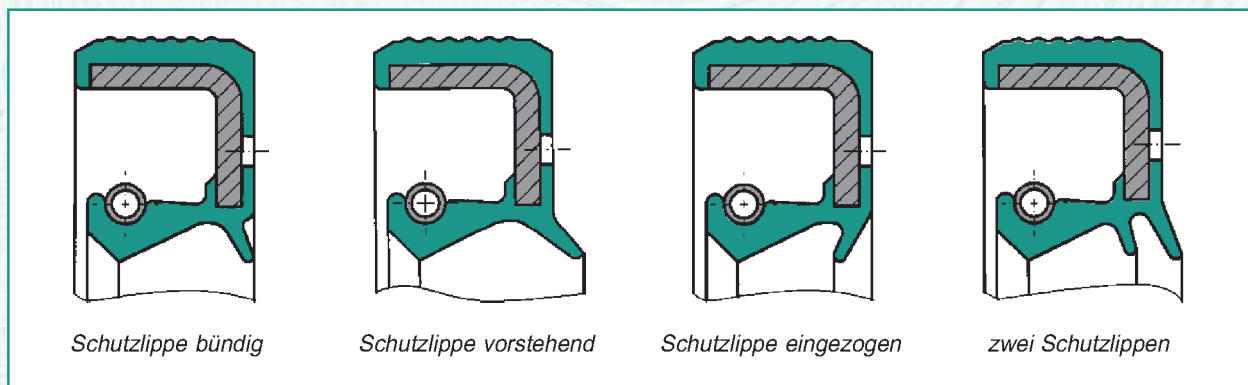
Ausführungsformen von Schutzlippen an RADIA®-Wellendichtringen
